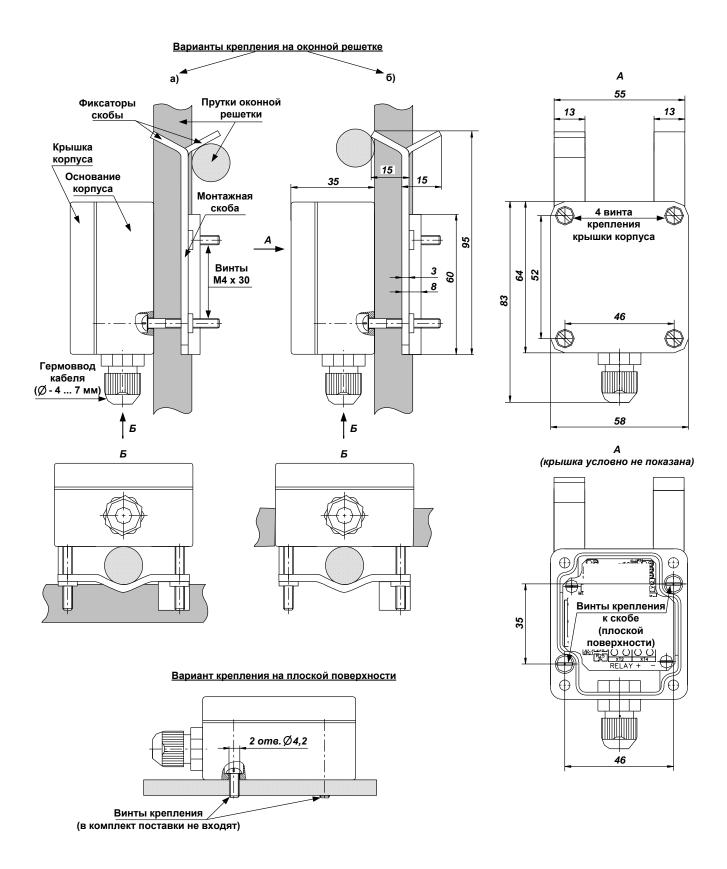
Внешний вид, варианты крепления, габаритные и установочные размеры.
